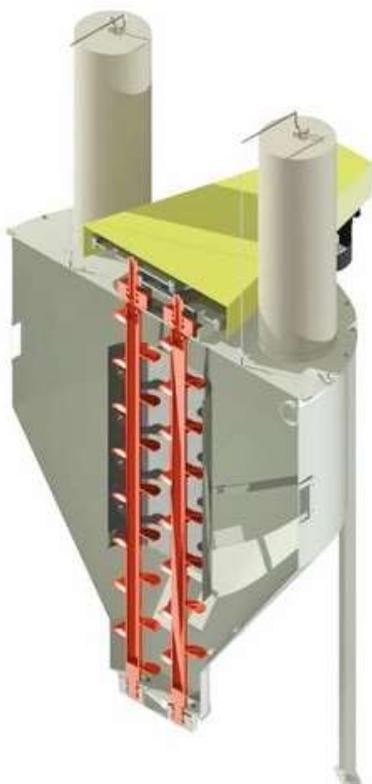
Вертикальный двухшнековый смеситель в разрезе
